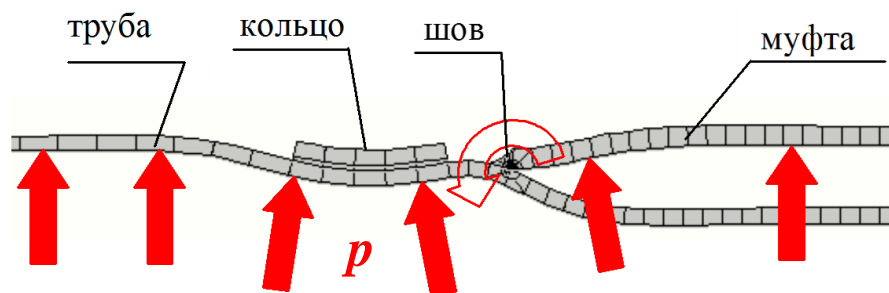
Схема разгрузки углового шва гладкой муфты разгрузочным кольцом
